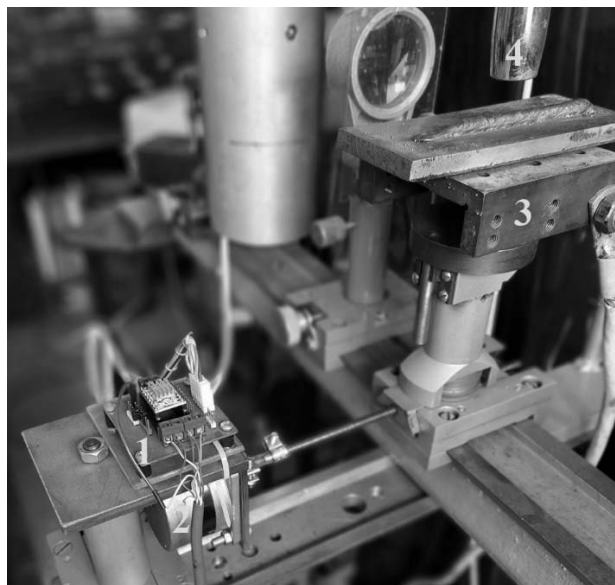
Электропривод движения свариваемых деталей: 1 – плата управления; 2 – шаговый двигатель; 3 – сварочный стол; 4 – сварочная горелка
